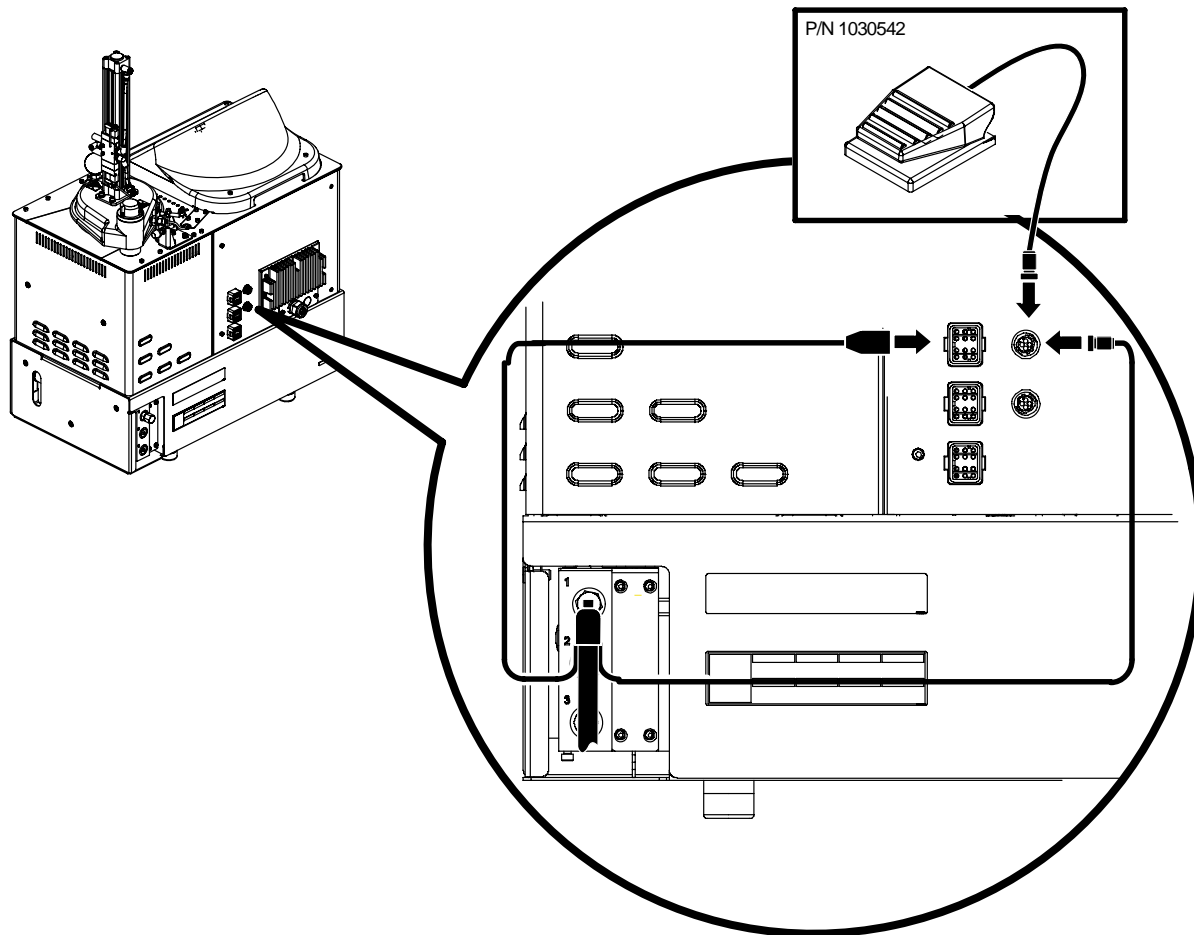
Schlauch für Handpistole mit Schalter oder Fußschalter anschließen
